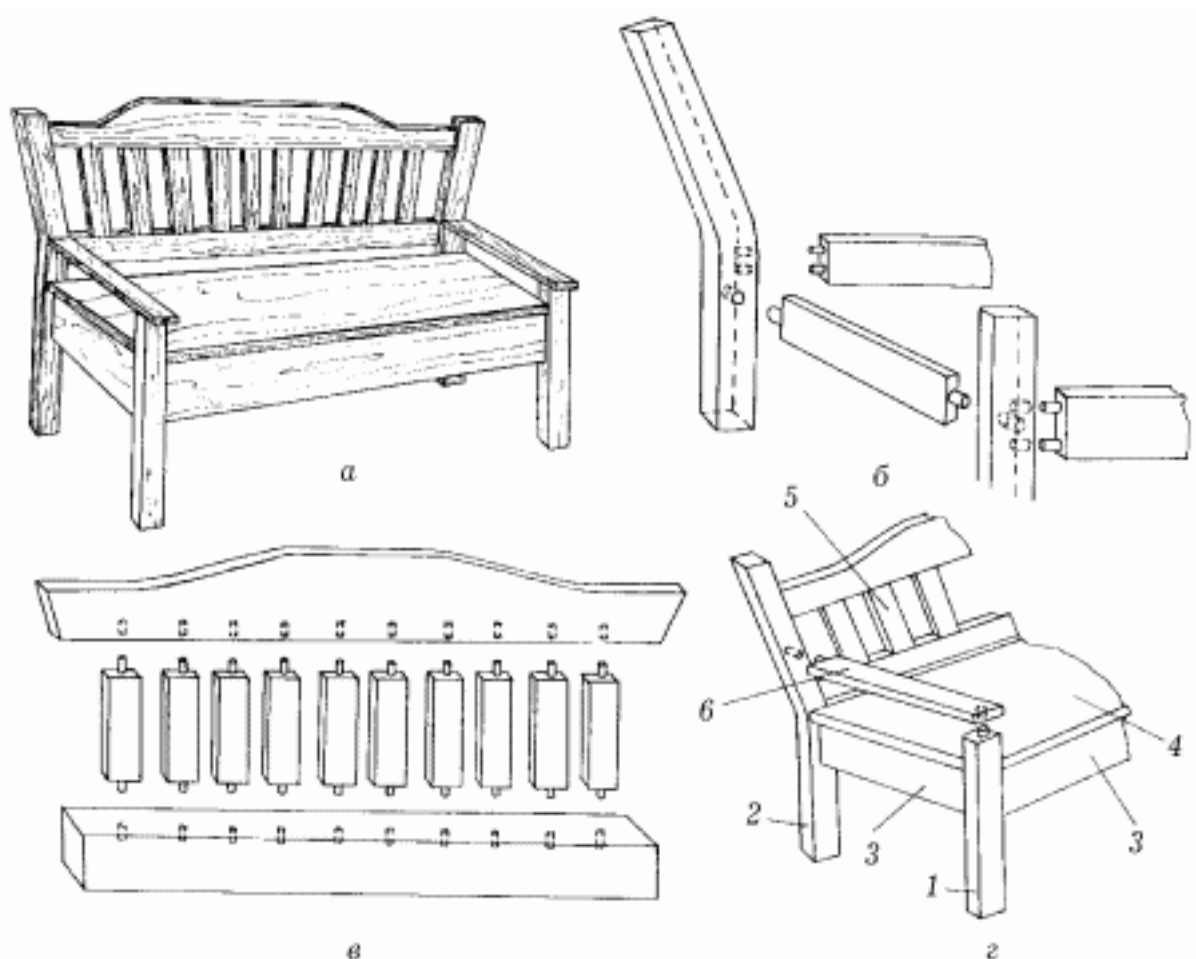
Классическая скамейка: а – общий вид; б, в, г – этапы сборки; 1 – ножка; 2 – ножка-упор; 3 – царга; 4 – сиденье; 5 – спинка; 6 – подлокотник.
